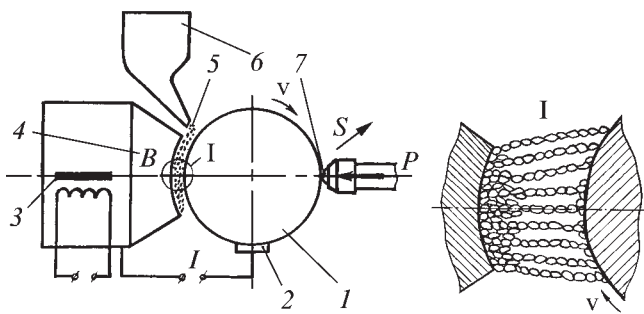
Электромагнитная наплавка с поверхностным пластическим деформированием (v – скорость главного движения; S – подача; P – сила деформирования; B – магнитная индукция; I – сила тока электродугowych разрядов):
